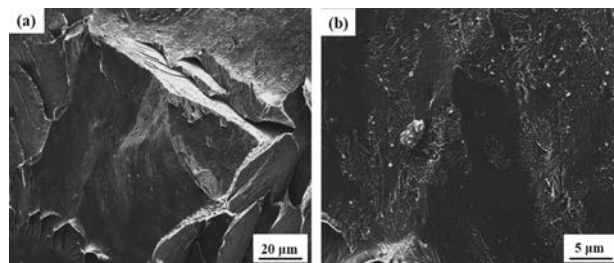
T-TIG-01-PWHT 焊接接头的拉伸断口: (a) 解理面; (b) 解理面放大形貌
